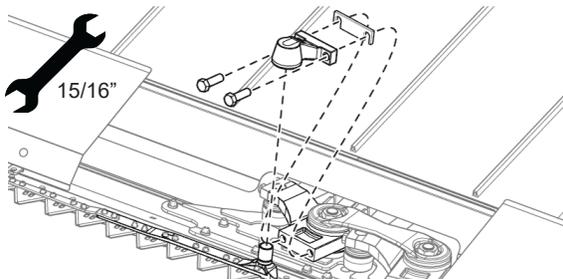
Retirar caja de cojinetes de la cabeza de la cuchilla derecha
